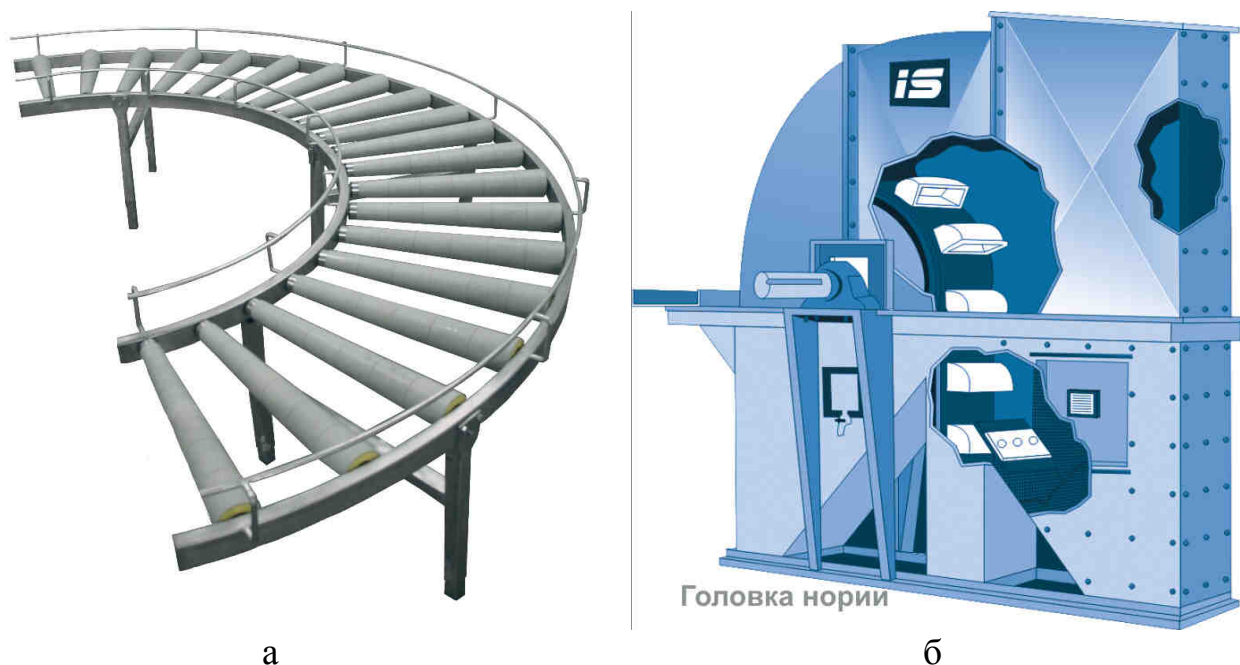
Загальний вигляд конвеєра: а – роликовий; б – ковшовий
